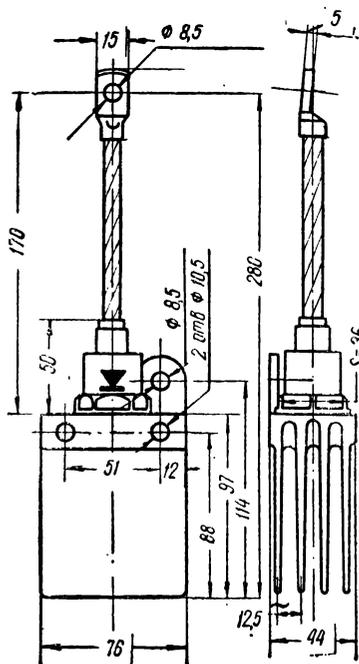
Габаритные размеры кремниевого вентиля ВК-50
